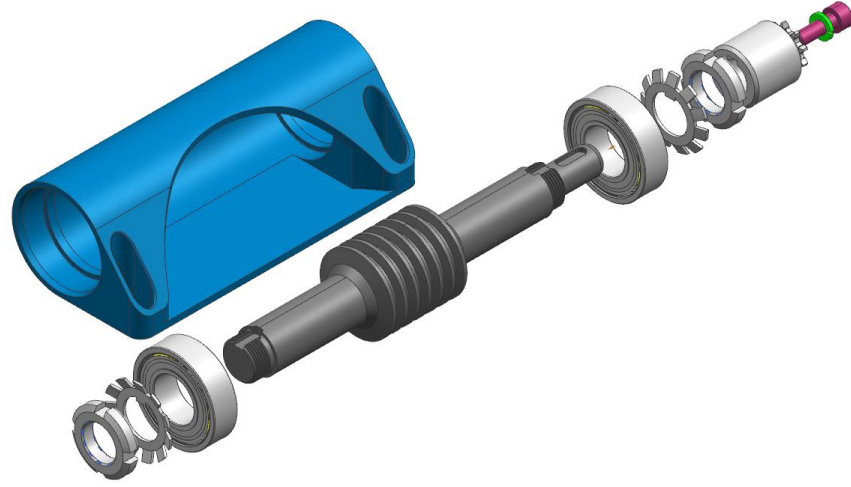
Pan grubu motor tork aktarım dişlisi
